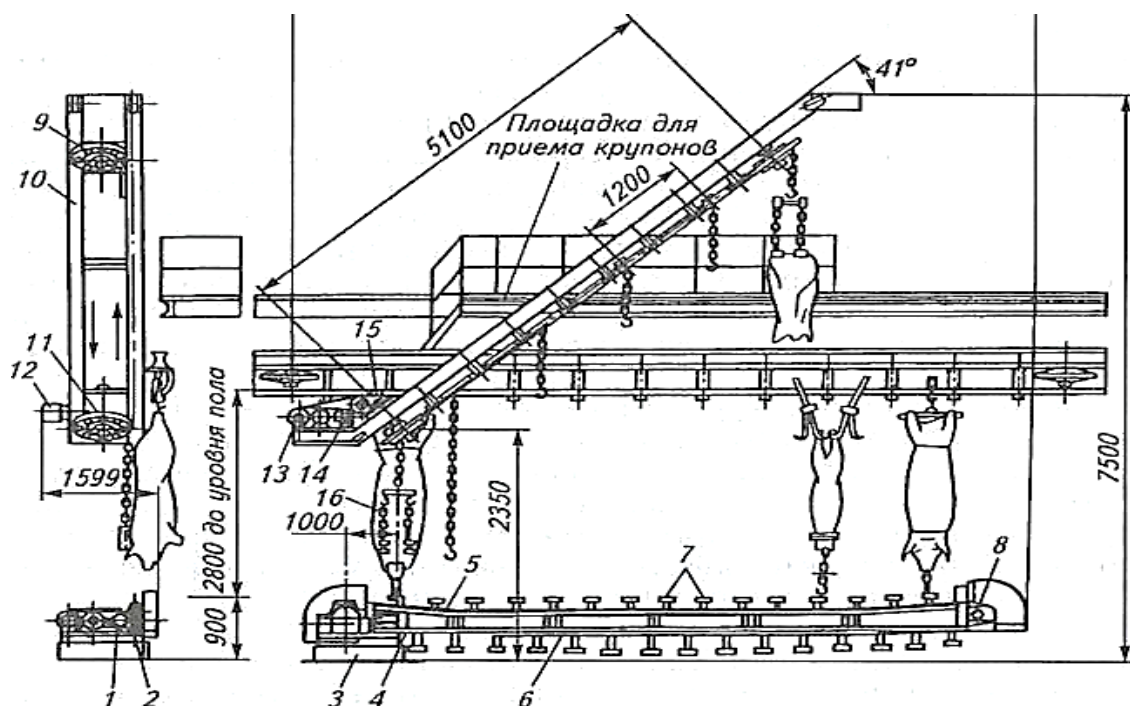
Схема агрегата В2-ФШН для снятия шкур и крупнонов со свиных туш и шкур с туш мелкого рогатого скота: 1 – вариатор; 2 – червячный редуктор; 3 – сварная рама; 4, 12 – электродвигатели; 5 – каркас конвейера натяжки и фиксации туш; 6 – пластинчатая цепь; 7 – фиксаторы туш; 8 – звездочка конвейера фиксации туш; 9, 11, 13 – блоки звездочек; 10 – наклонный конвейер; 14 – вариатор; 15 – червячный редуктор; 16 – цепь с захватами
